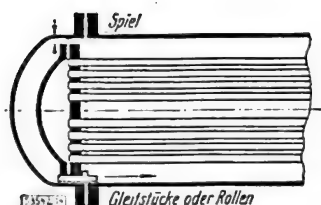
Hinterer Rohrboden mit Gleitstücken oder Rollen
